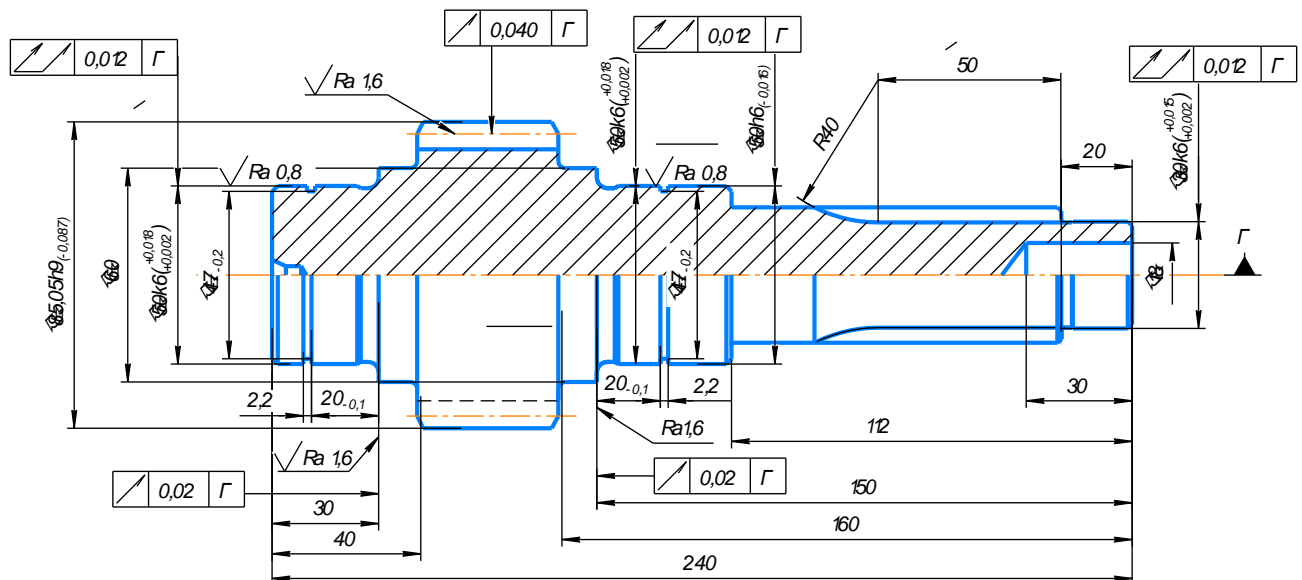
Фрагмент детали «Вал-шестерня»
